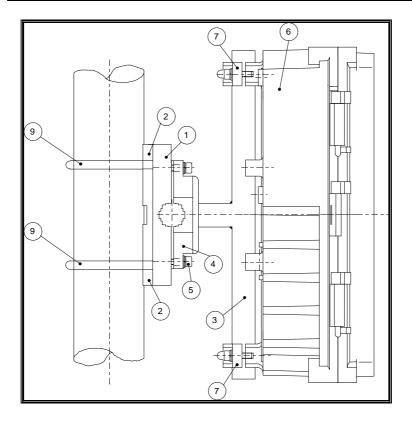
Vista lateral PRU con los detalles del montaje en tubo
